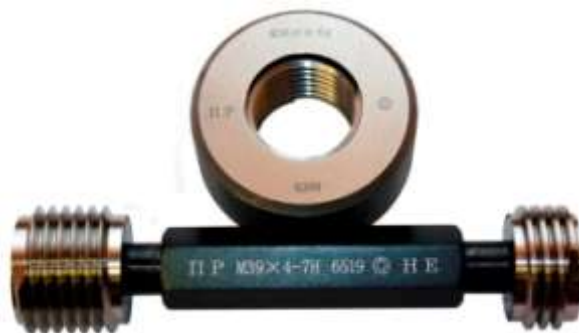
Резьбовые калибр-пробка и калибр-кольцо
